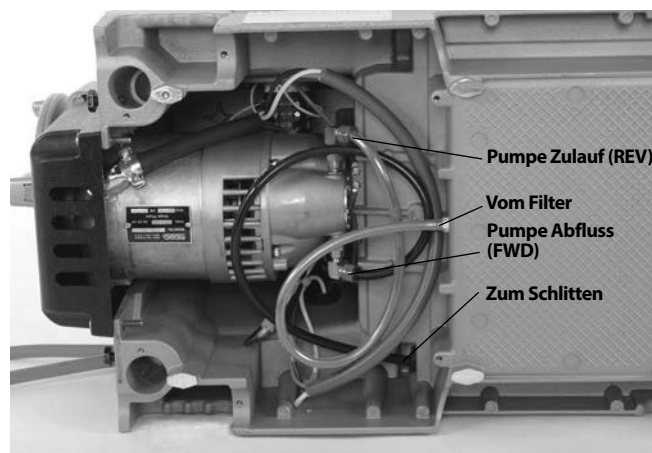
A – Ölpumpenanschlüsse für das Schneiden von Linksgewinden (Schalter auf REV)
